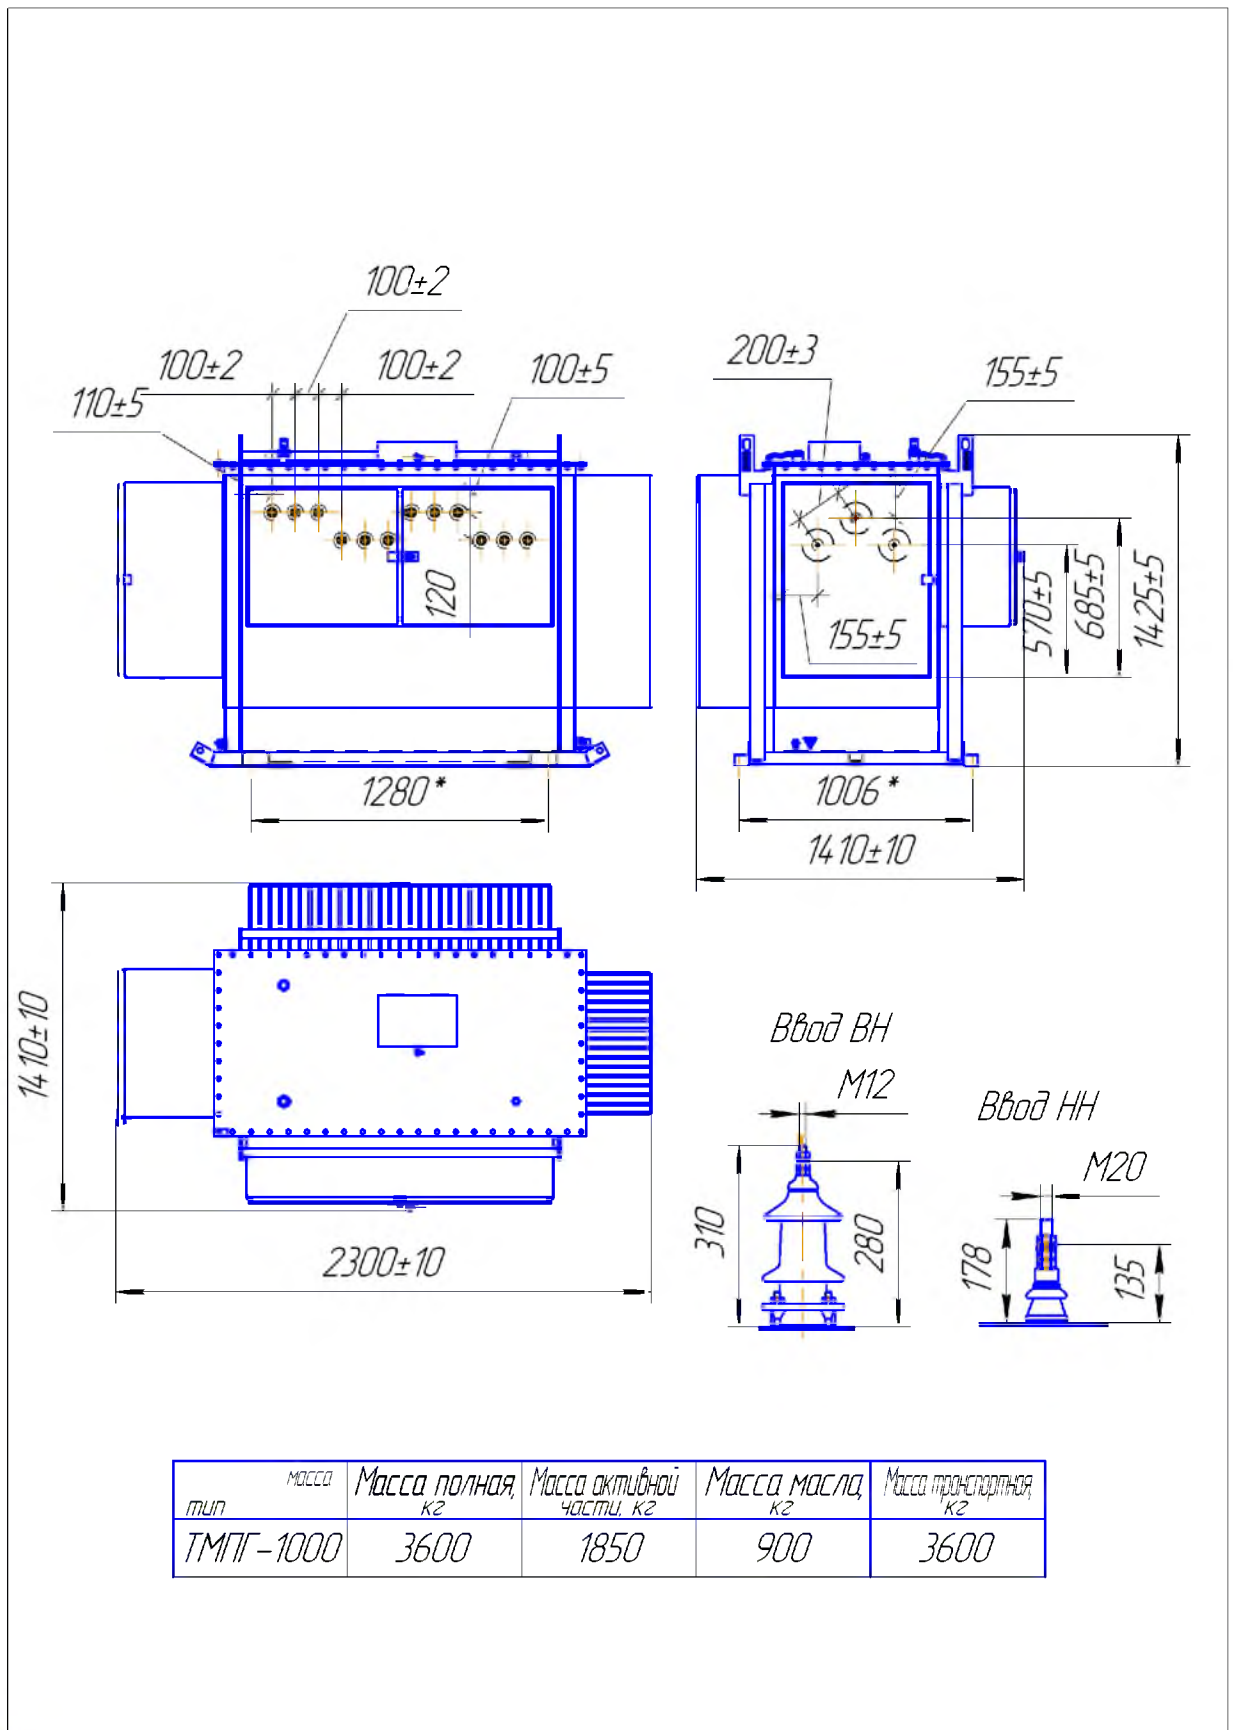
Габаритные, установочные и присоединительные размеры трансформаторов ТМПГ-СЭЦ-1000
